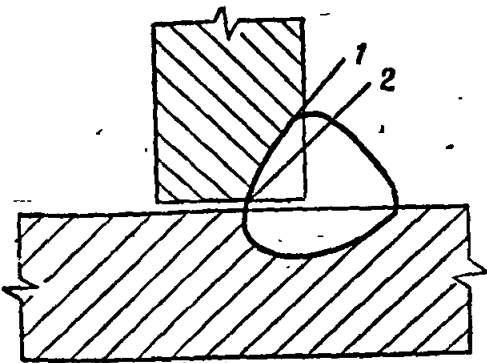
а. Схема расчетных сечений сварного соединения с угловым швом 1 — сечение по металлу шва, 2 — сечение по металлу границы сплавления
